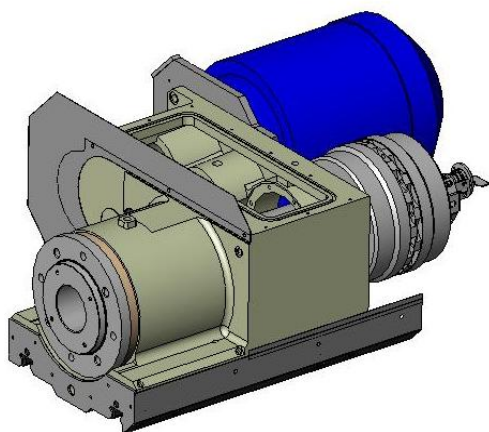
3D конструкція шпиндельної бабки верстата
